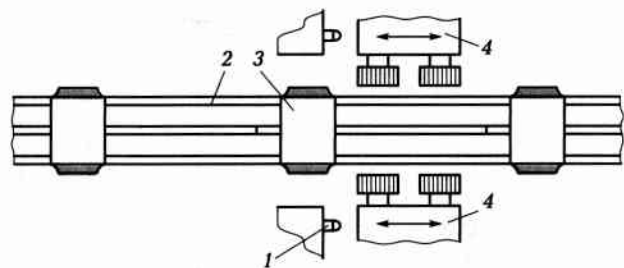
Схема обработки корпусной детали на автоматической линии
